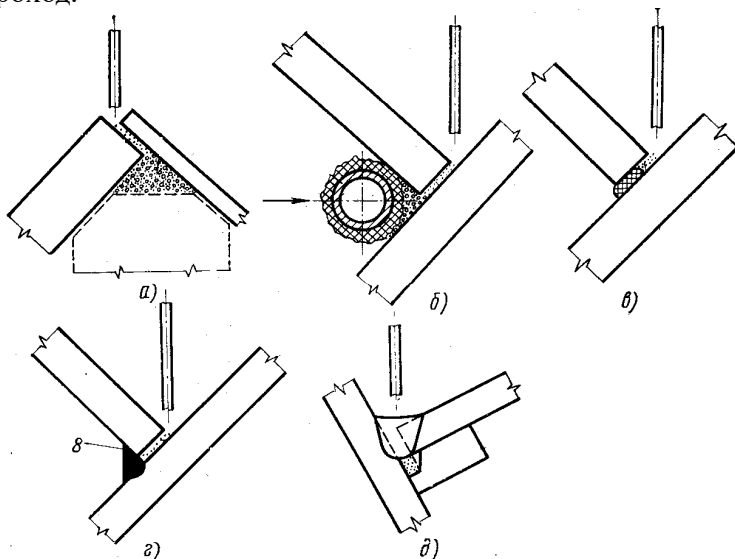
Схема способов сварки под флюсом угловых и тавровых швов:
